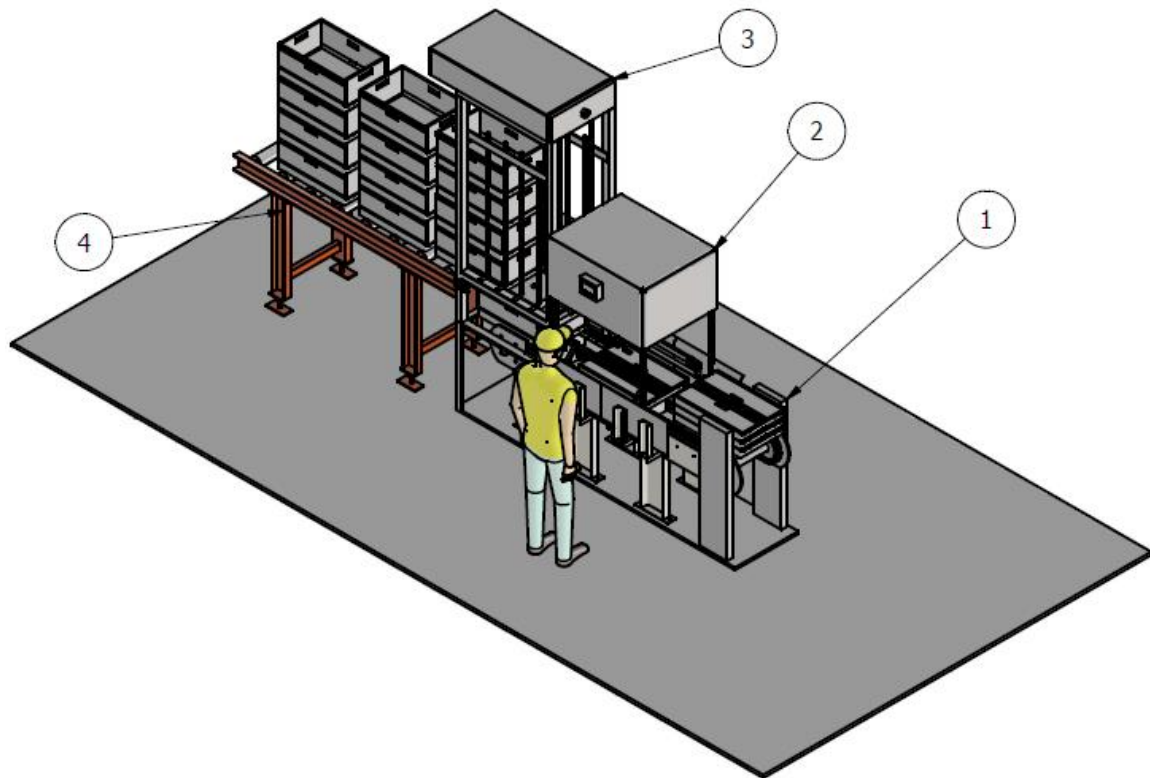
Diseño 3D de la maquina ensambladora de gavetas plegables: (1) El ingreso de una pila de gavetas cerradas, (2) Mecanismo de ensamble de gavetas, (3) Acopiamiento de gavetas abiertas y (4) Deposito de pilas de gavetas
